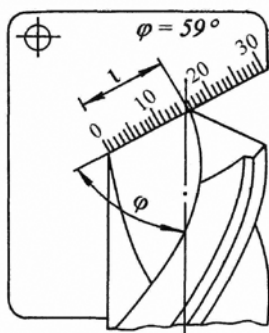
Измерение главной режущей кромки сверла шаблоном
